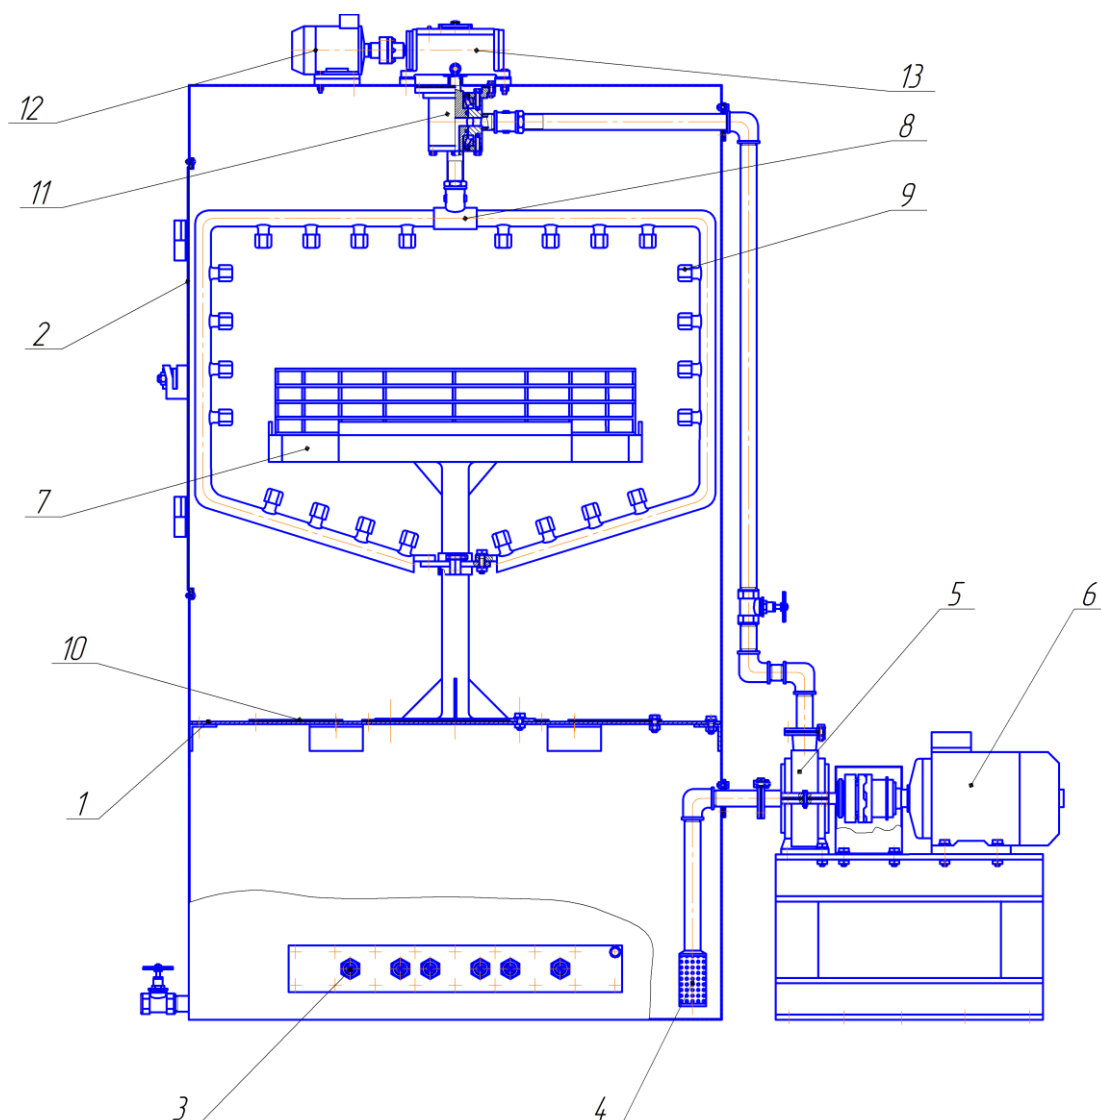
Схема установки для мойки агрегатов: 1-перегородка; 2-корпус; 3-тэн; 4-фильтр; 4-насос; 6,12-электродвигатели; 7-стол; 8-рама; 9-форсунка; 10-фильтрующая сетка; 11-гидромуфта; 13-редуктор;
